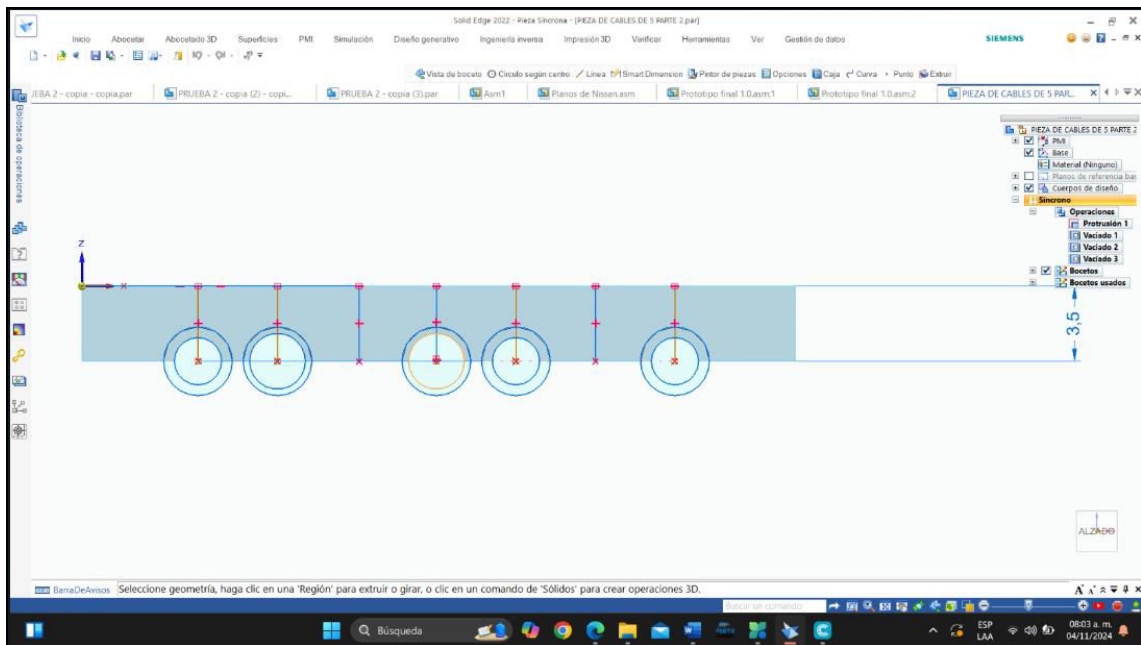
Primer diseño Tapa de 5 cables Vista Alzado
